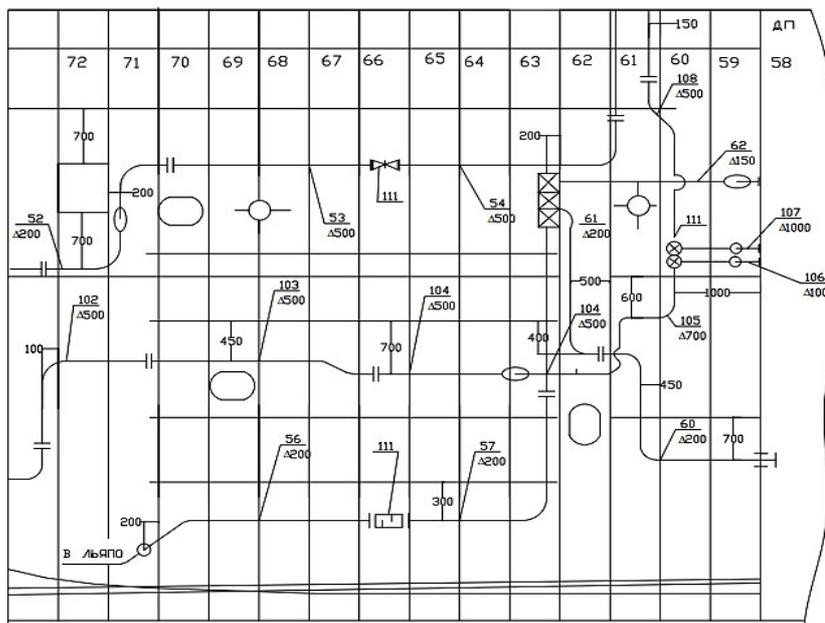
Сборочно-монтажный чертеж трубопровода с координатами трасс
